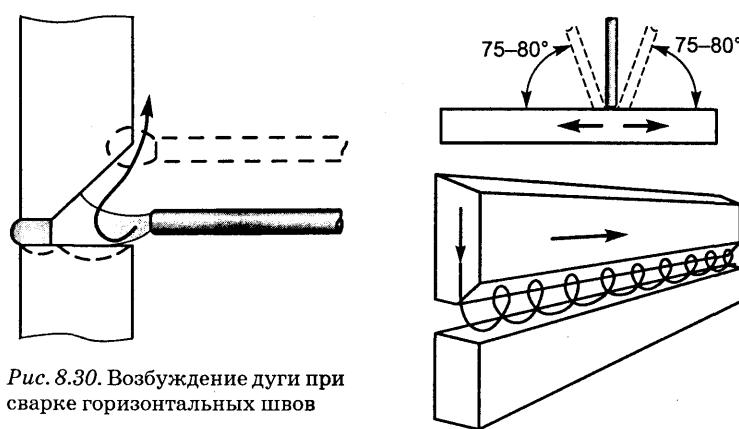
Возбуждение дуги при сварке горизонтальных швов
